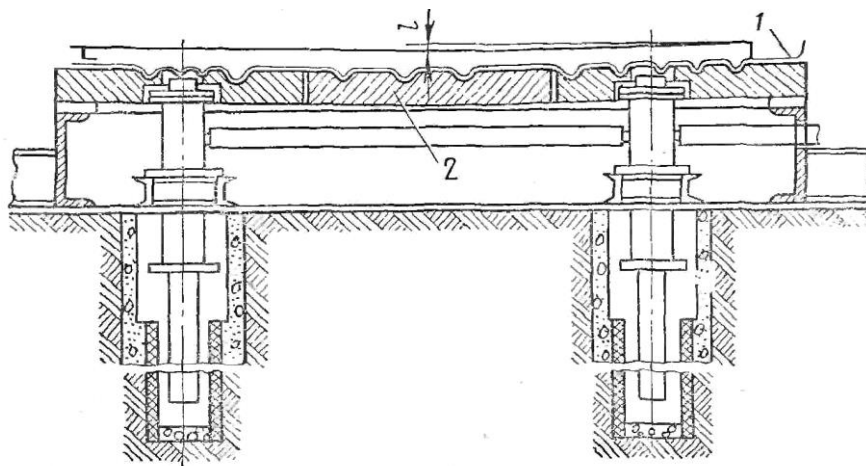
Стенд для прогиба обшивки перед сваркой:
